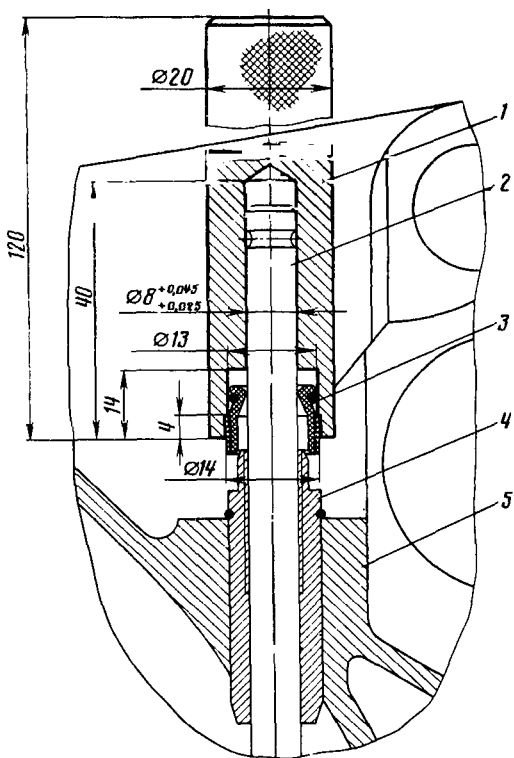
Оправка для запрессовки маслоотражательного колпачка клапана:
